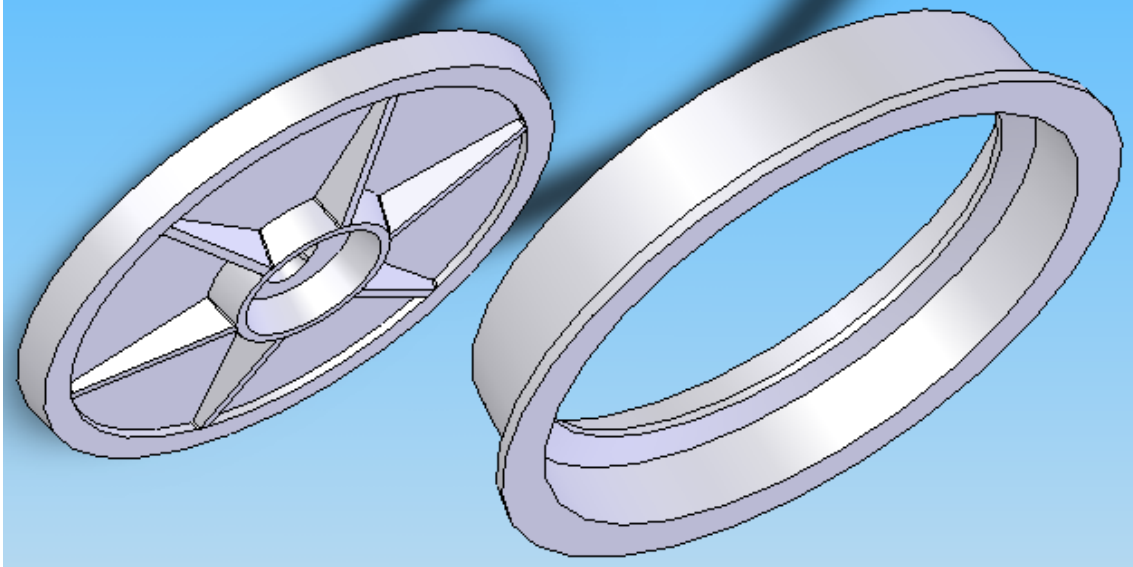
Ensamble de la tapa de inspección sobre su cerco.
